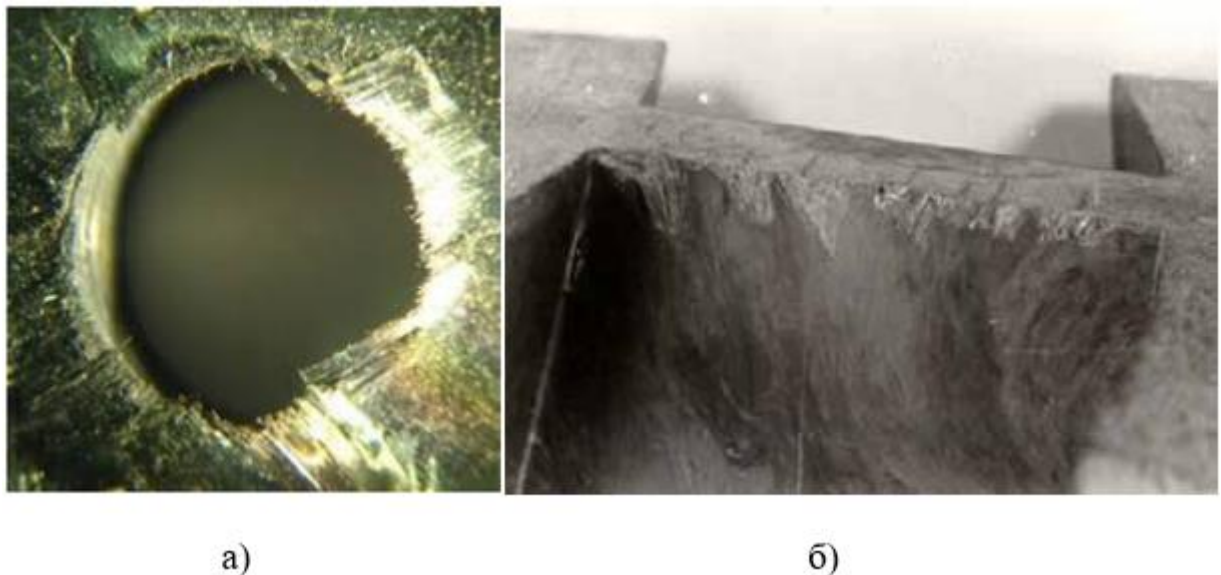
Дефекти поверхонь композиційних матеріалів від лезового інструменту: а) від свердління; б) після фрезерування
